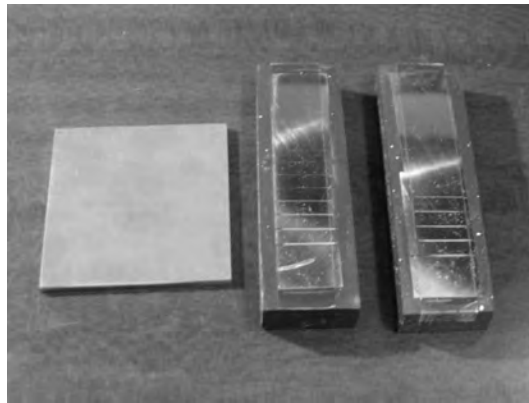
Тестовые ОК: сварные пластины и калибровочные щели.
